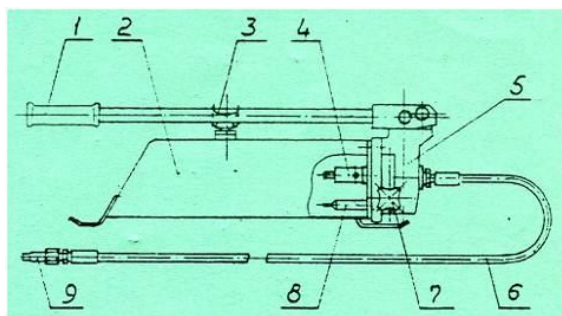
Насос ручной: 1 – рукоять; 2 – маслобак; 3 – пробка с замком; 4 – предохранительный клапан; 5 – корпус насоса; 6 – рукав высокого давления; 7 – рукоятка управления сливного клапана; 8 – фильтр; 9 – гидравлическая полумуфта
